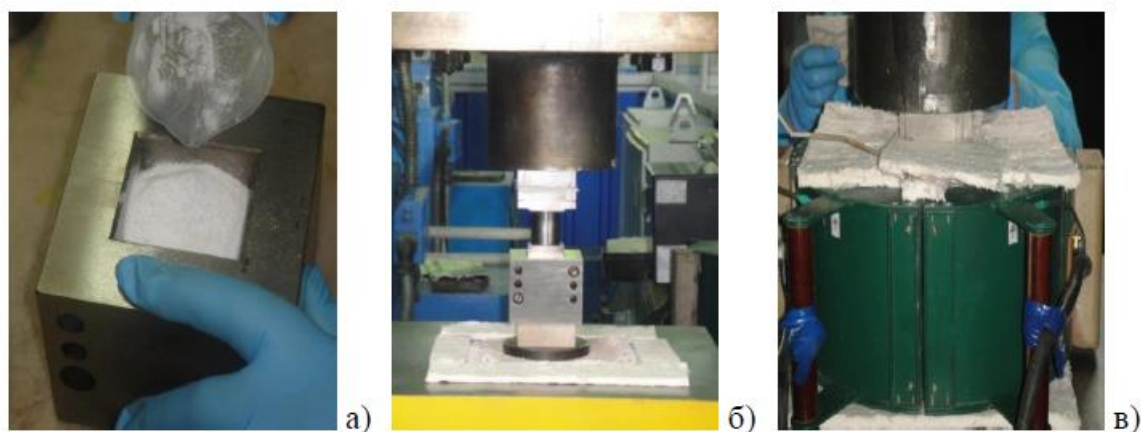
Поэтапные шаги подготовки образца методом горячего прессования (а) порошок, б) пресс-форма, в) пресс для компрессионного спекания
